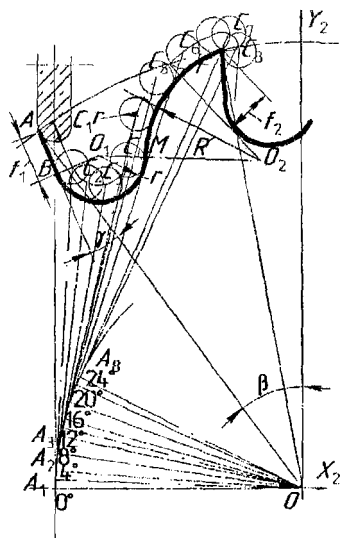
Схема обработки профиля зуба пилы на станке фирмы Lorch
